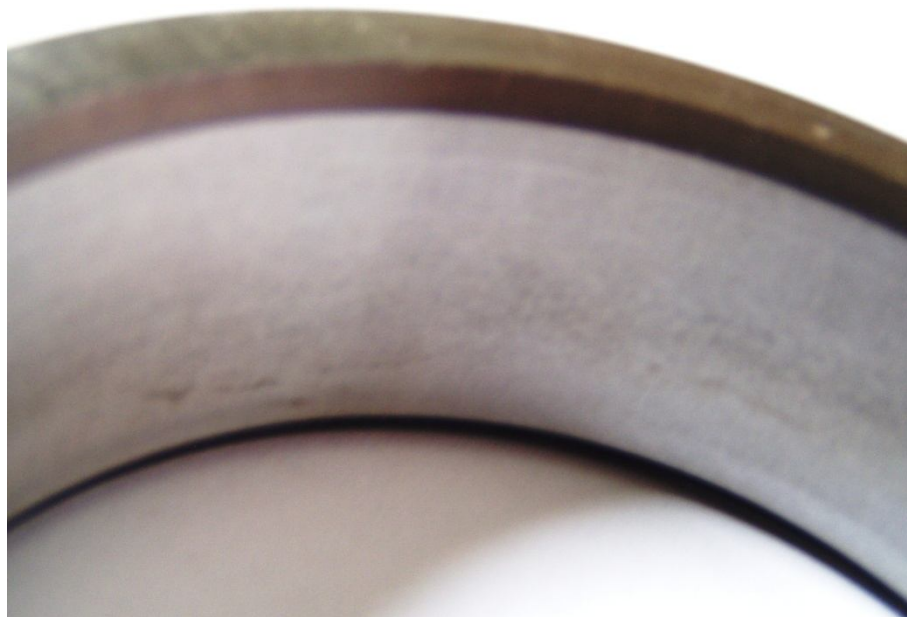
Матовая поверхность внутреннего кольца подшипника при неподвижной посадке на вал
